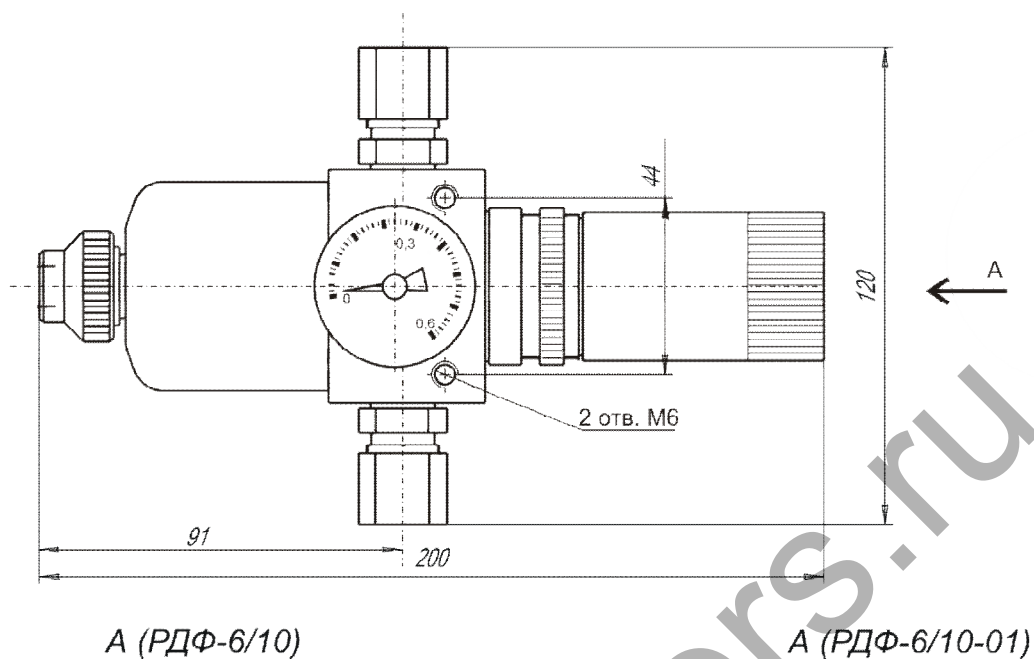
Габаритные и установочные размеры редуктора с верхним пределом регулируемого давления 0,6 МПа
